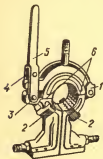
Разъемный индуктор для закалки способом одновременного нагрева с рычажным зажимом и магнитной цепью для выравнивания нагрева детали в местах токоподводов:
